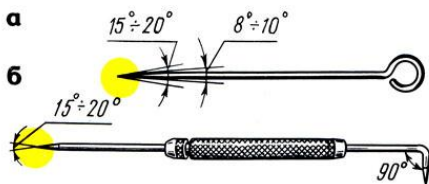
Чертилки: а - круглая, б - с отогнутым концом
